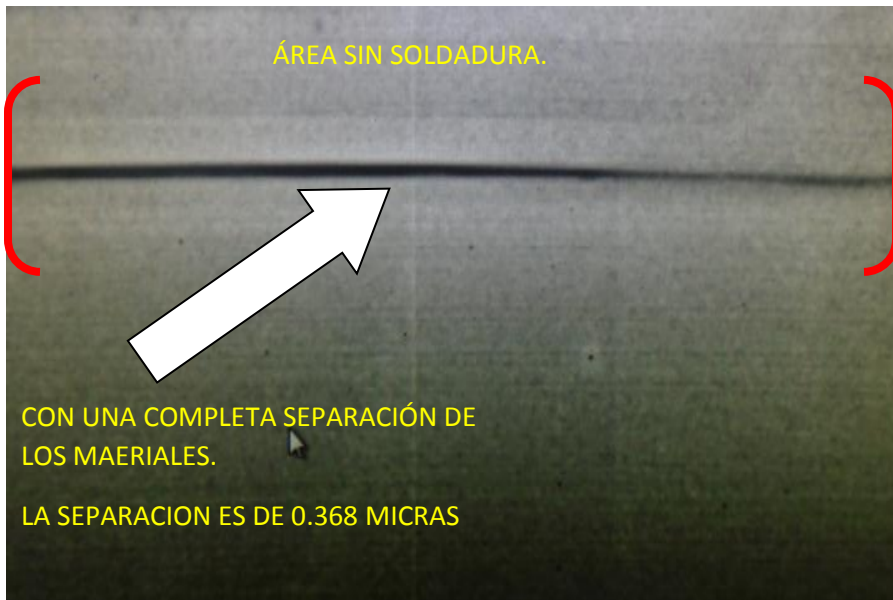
Sin cordón de soldadura. (Rechazado)
